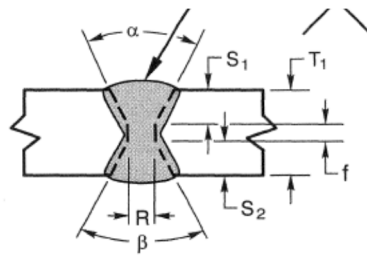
Parámetros geométricos de la soldadura a tope
